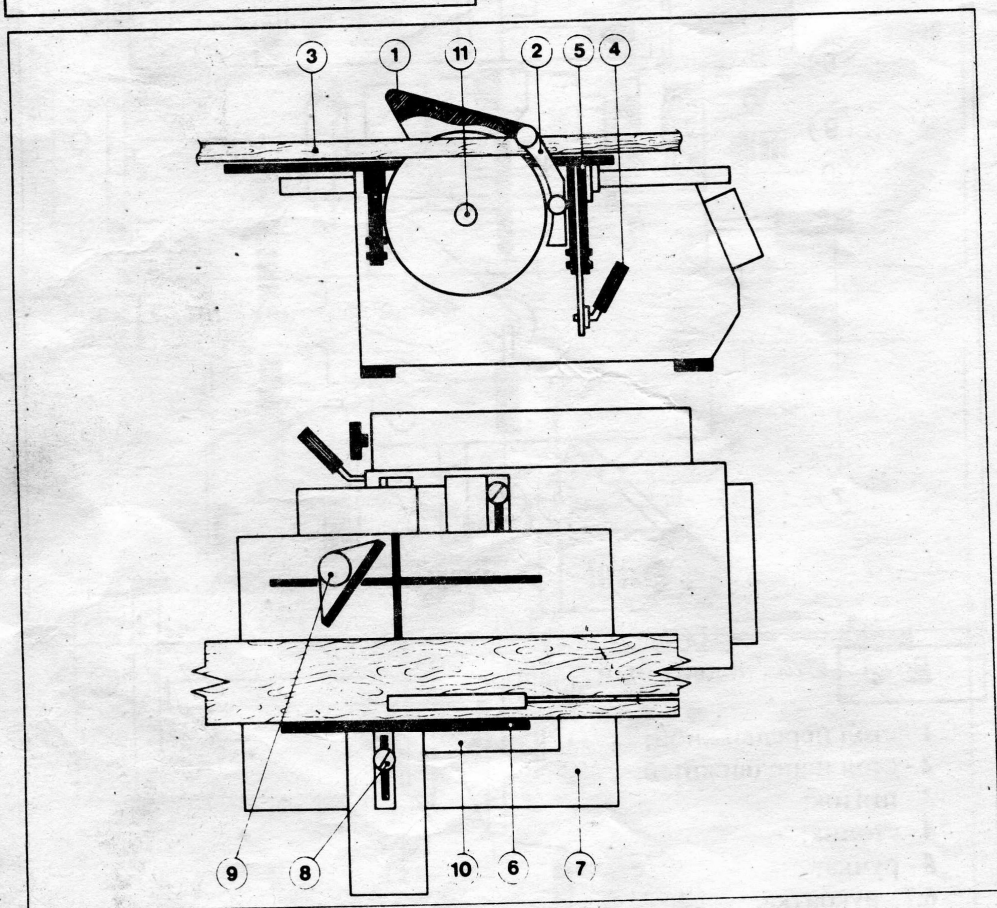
Стол пильно-фрезерный (стол подвижный условно не показан)
